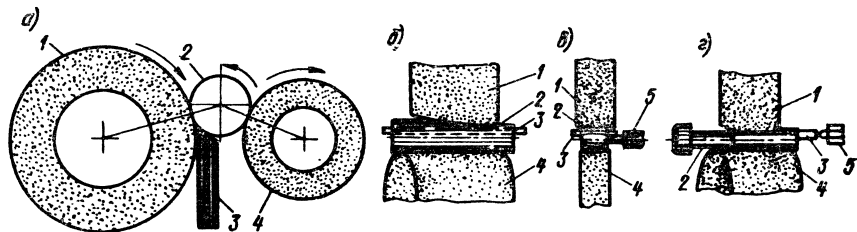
Схемы установки (а) и бесцентрового наружного шлифования (б—г): 1 — шлифовальный круг; 2 — обрабатываемое изделие; 3 — опорный нож; 4 — ведущий круг; 5 — упор
